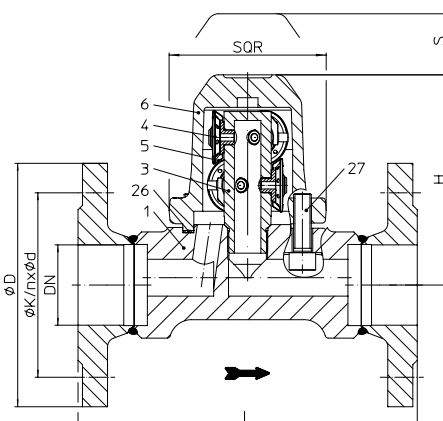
1....6K2 (DN40-50) com 6 cápsulas, com flanges
